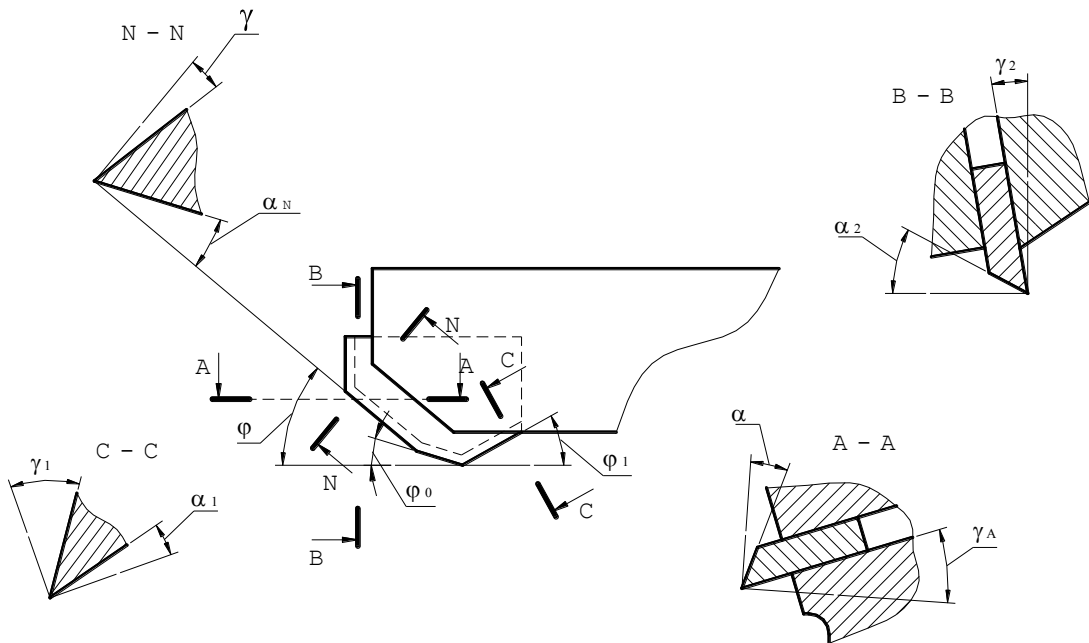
Геометрические параметры режущей части торцевой фрезы
